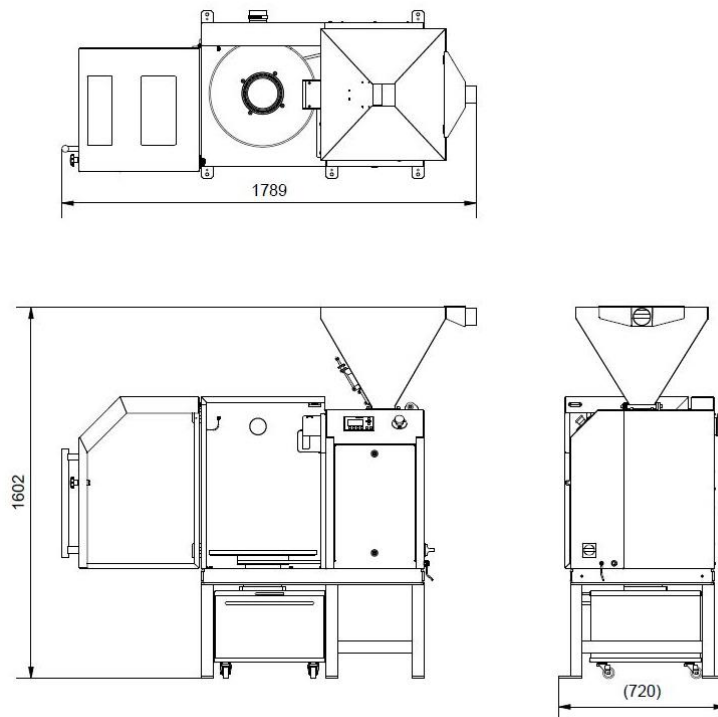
Gehäusetür geöffnet – Trichter 60 Liter
